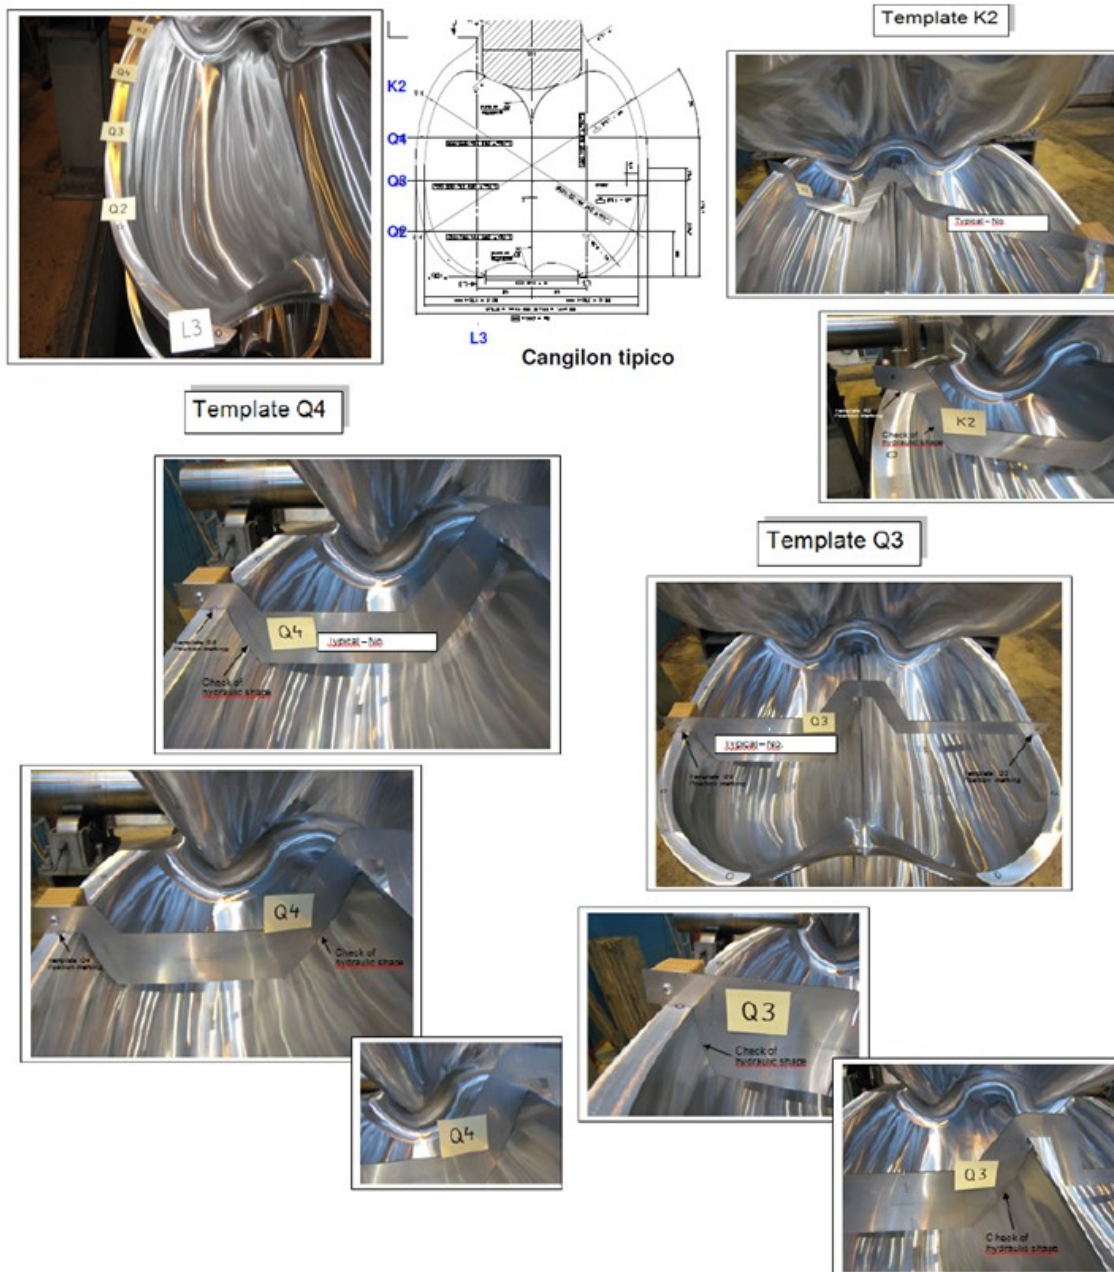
Plantillas Q2,Q3,Q4 utilizadas para medir la pérdida del perfil de cangilón.
